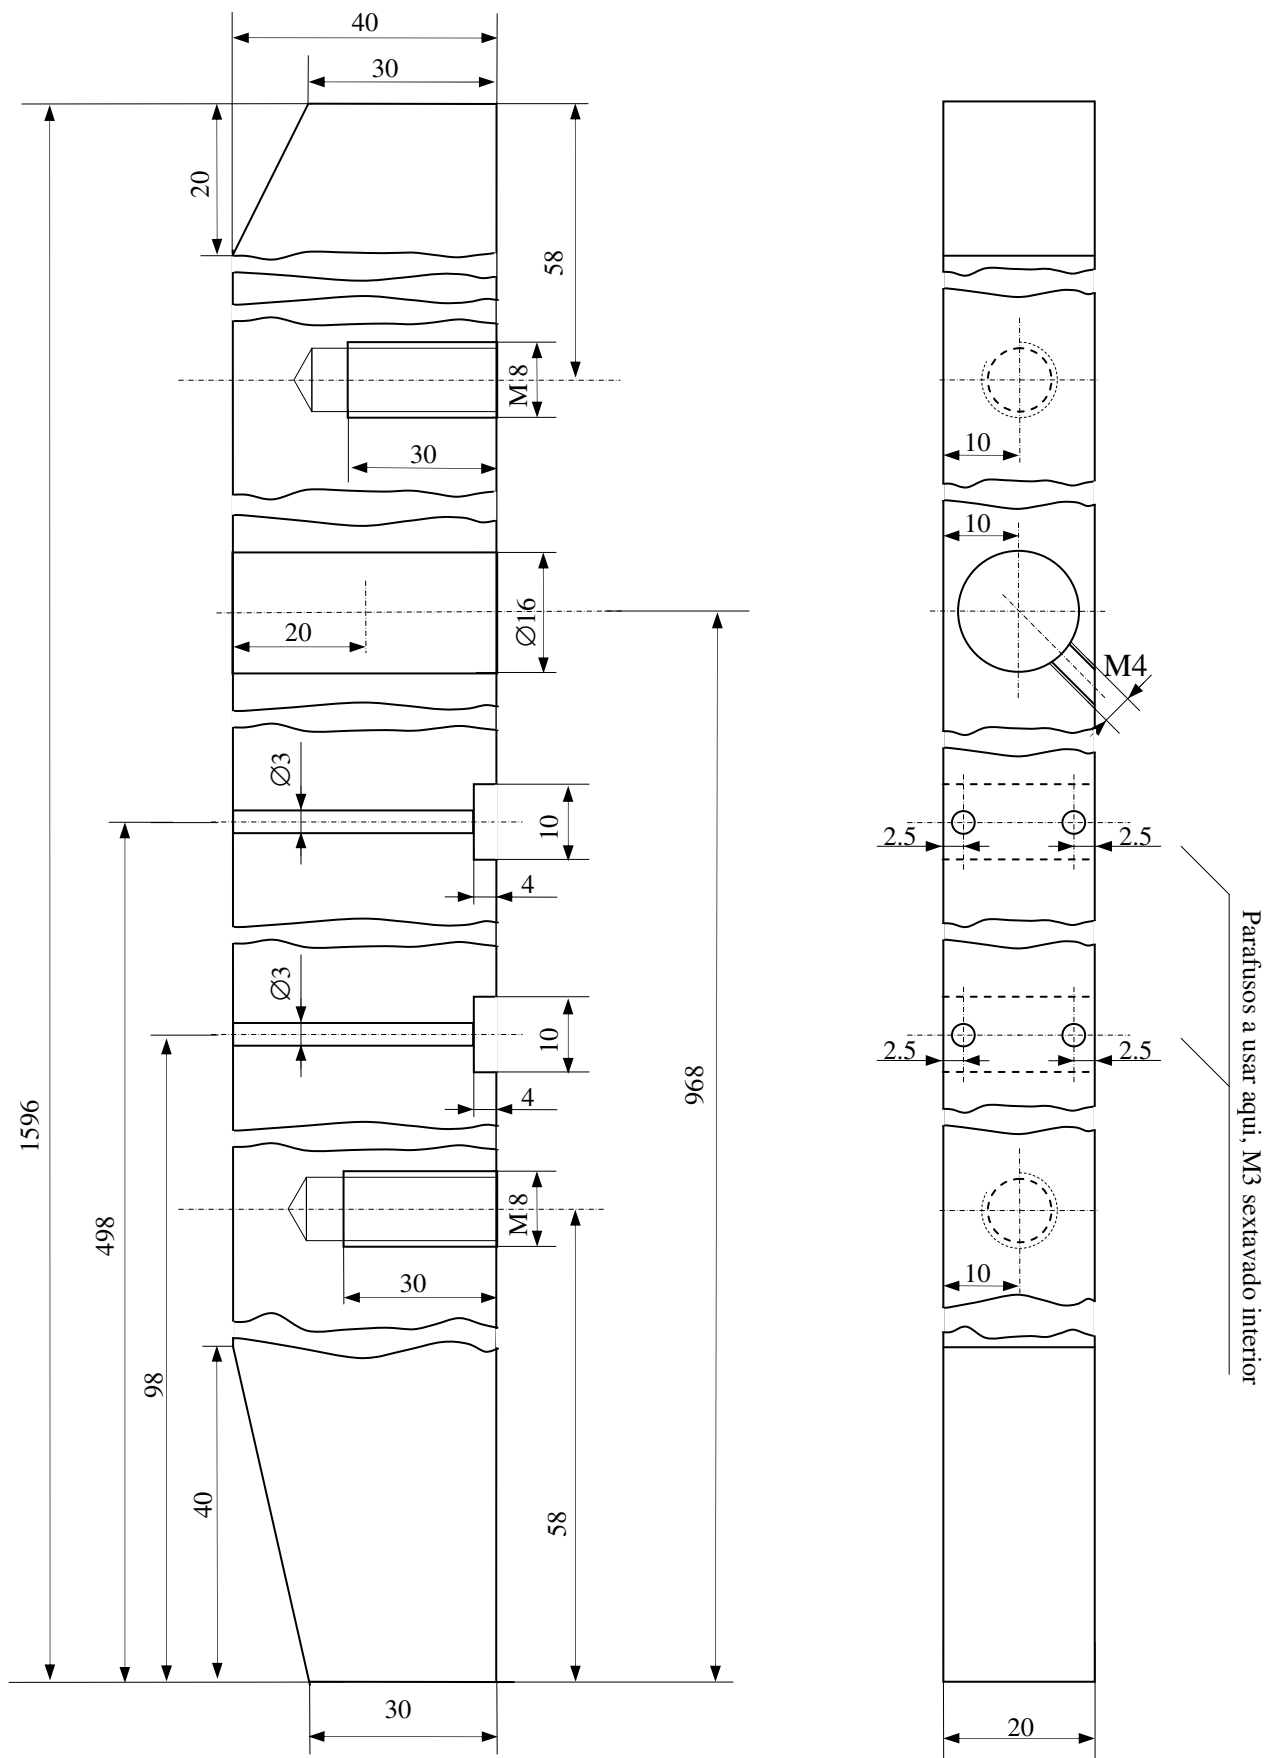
Suporte para as secções de 160 e 40 mm.
